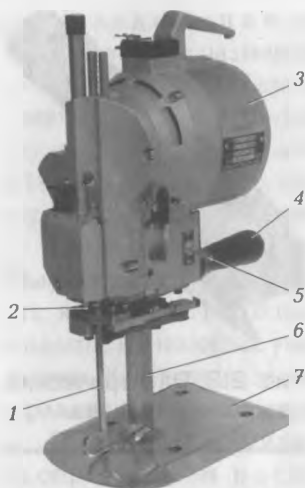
Передвижная раскройная машина с вертикальным ножом:
